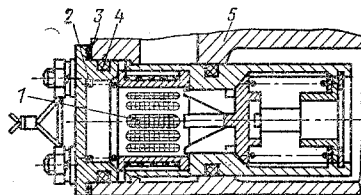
Фильтр редукционного клапана верхнего маслоагрегата:
